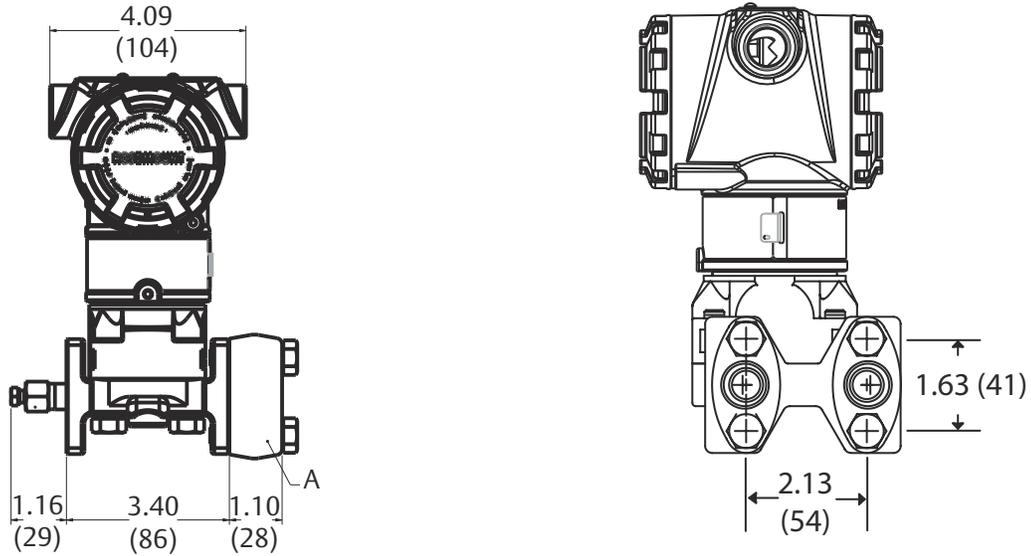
Coplanar Flansch mit optionaler Montagehalterung (B4) für 2 in.-Rohr- oder Wandmontage
